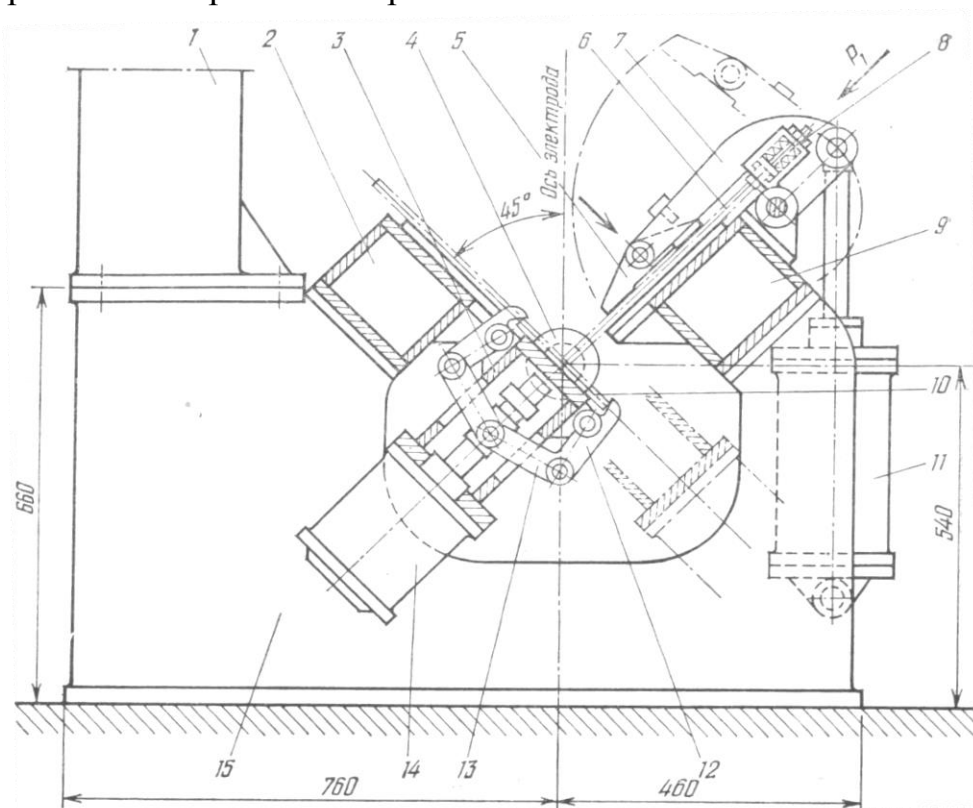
Кондуктор–кантователь для сборки и сварки тавровых балок
